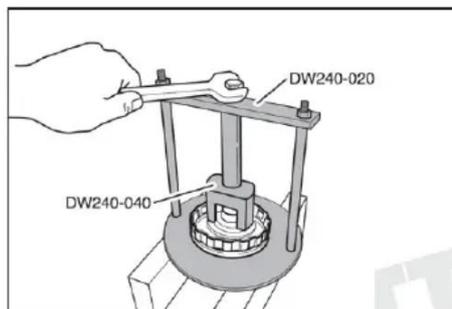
Tambores de embreagem na própria carcaça da caixa
